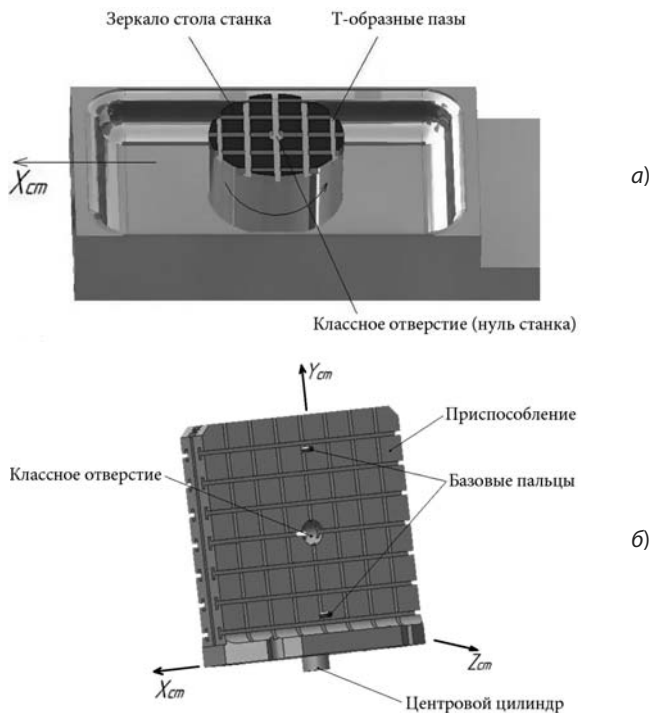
Установка приспособления на стол фрезерного станка: а — стол станка; б — приспособление
